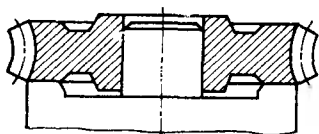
Схема установки колеса червячной передачи при нарезании зуба — правильная
